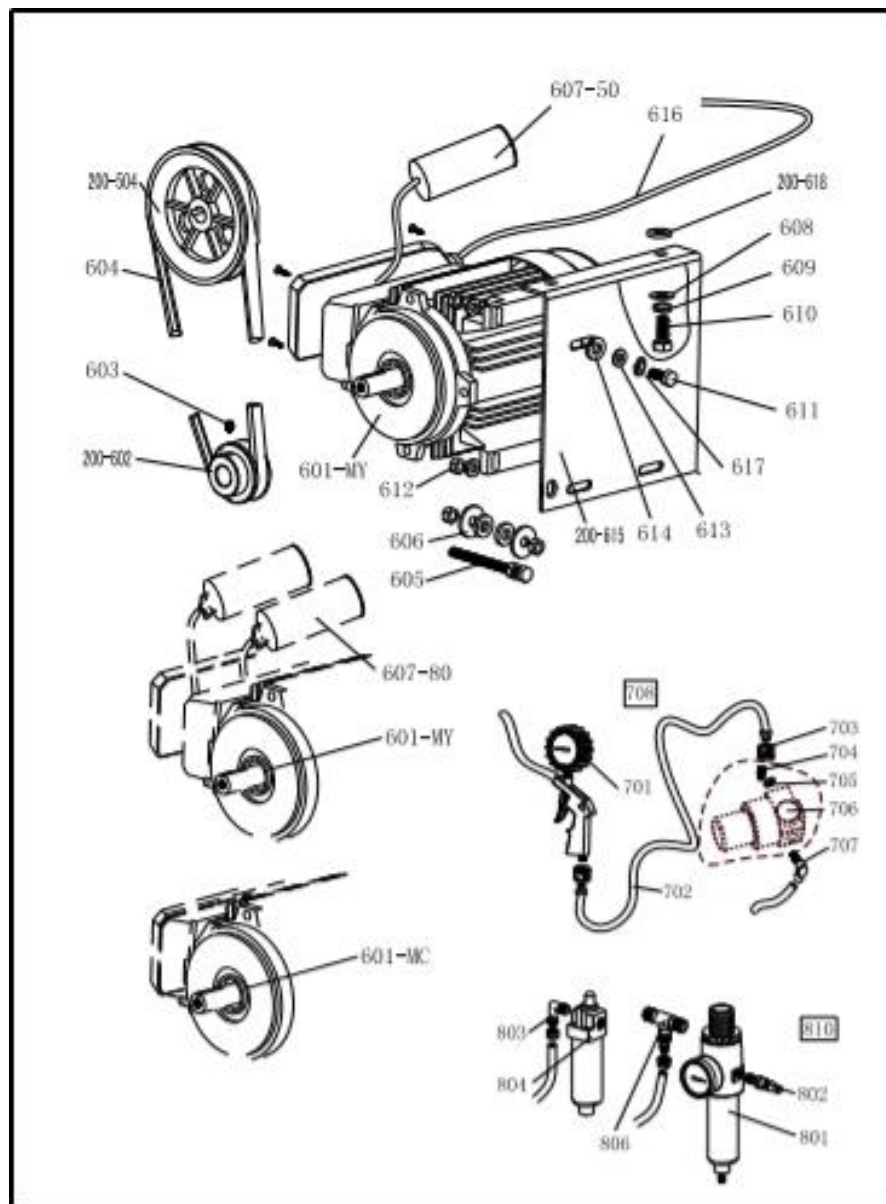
Explosionado del conjunto motor y de elementos neumáticos
